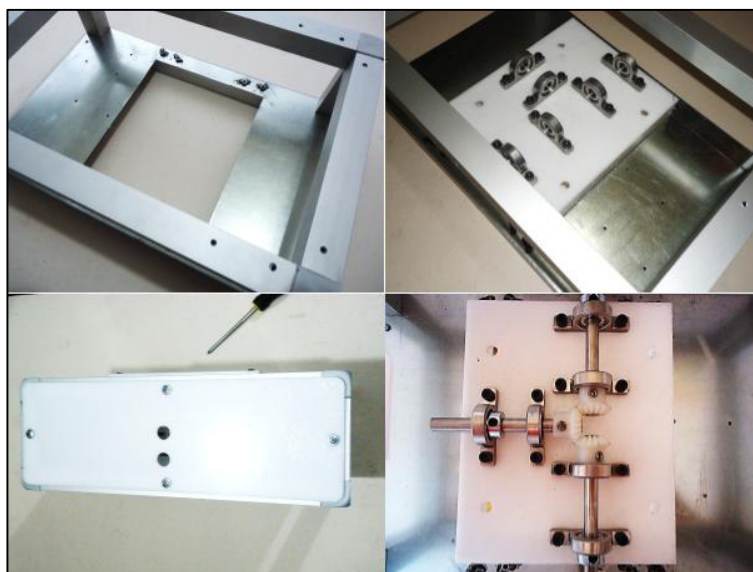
Ensamblaje y montaje de la carrocería del robot.
